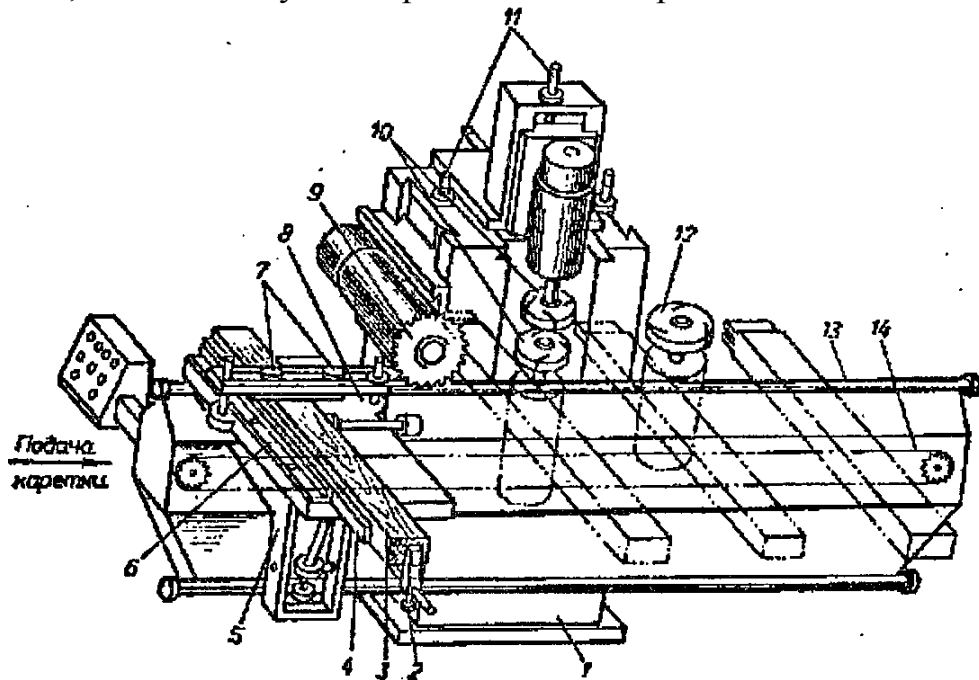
Односторонній шипорізний верстат для рамних шпильок: 1 – станина; 2 – торцевий упор; 3 – заготовка; 4 – підпирний брусок; 5 – зворотно-поступальна каретка; 6 – лінійка напрямної; 7 – гідропритискачі; 8 – супорт; 9 – пила для торцювання заготовок; 10 – шипорізні фрези; 11 – регулювальні гвинти; 12 – дискова пила для вироблення провущин; 13 – направляючі; 14 – ланцюгова передача.
